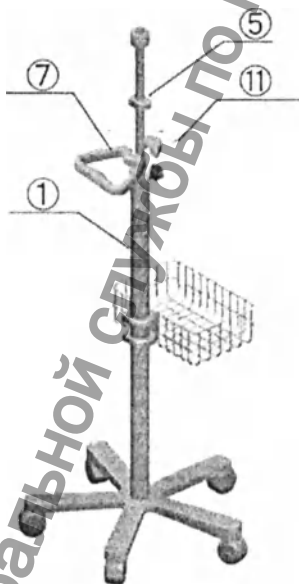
Сборка медицинской стойки Endostand Шаг 4
